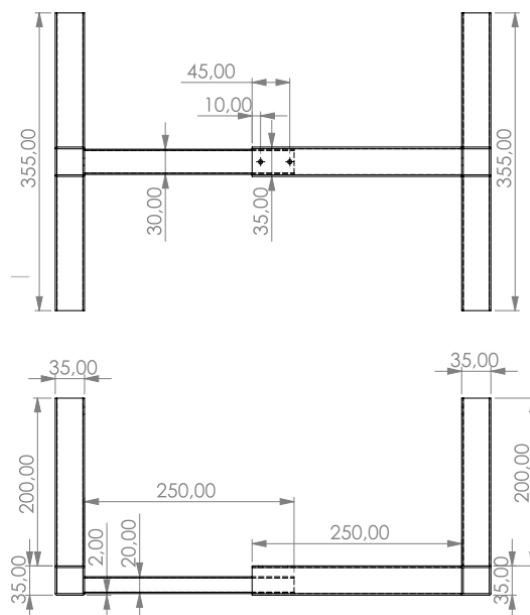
Technische Zeichnung der Halterung für Knochen als Teststand für die Impedanzmessungen. Alle Angaben sind im Millimeter.
